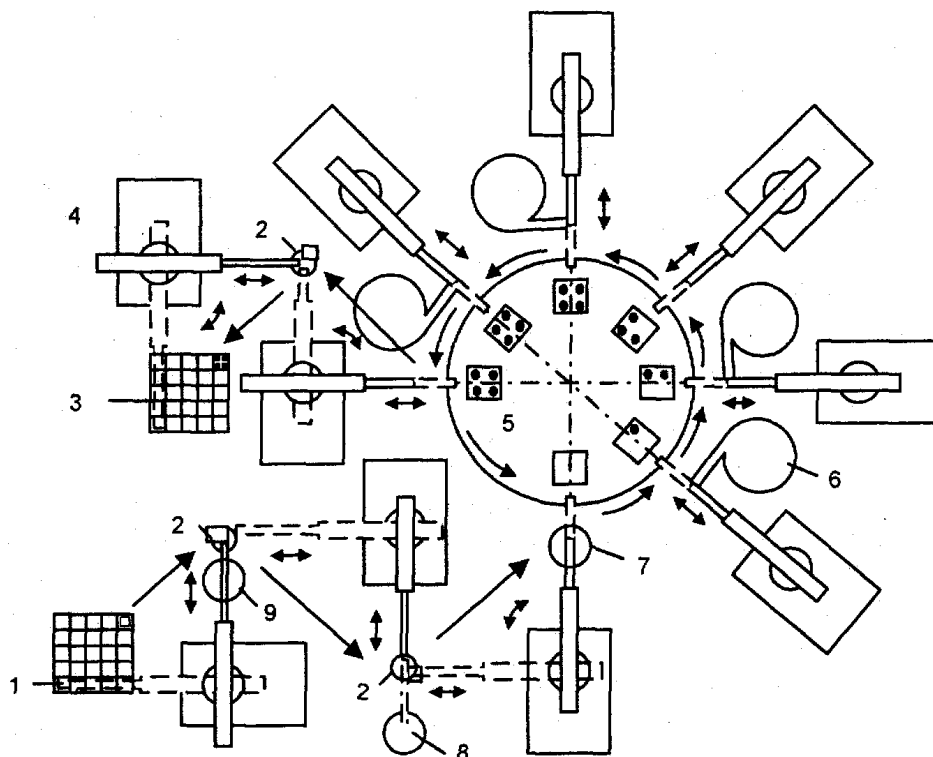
Робототехнический комплекс для сборки контурных катушек радиоприемников: 1 — загрузочное устройство (тара); 2 — промежуточная точка; 3 — разгрузочное устройство; 4 — устройство группового управления; 5 — роторный стол; 6 — виброзагрузочное устройство; 7 — ванна для очистки; 8 — ванна для пайки; 9 — ванна для флюсования
